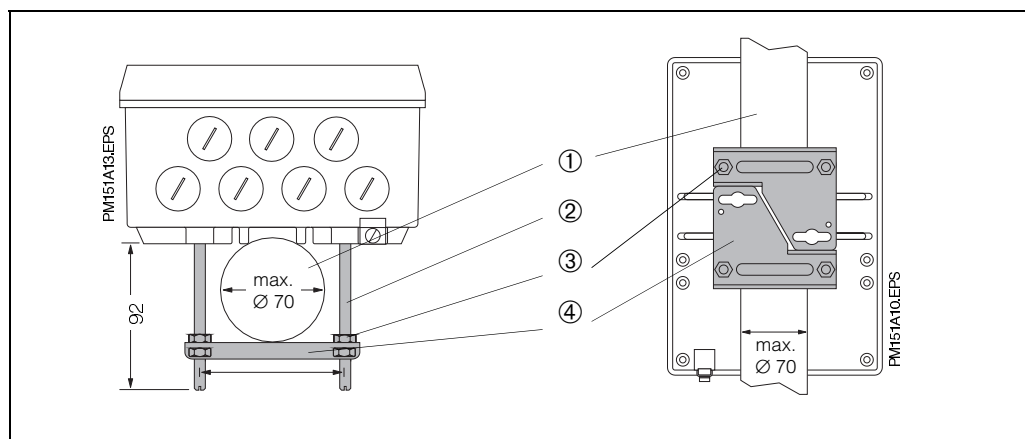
Montage du boîtier de terrain sur un mât vertical
